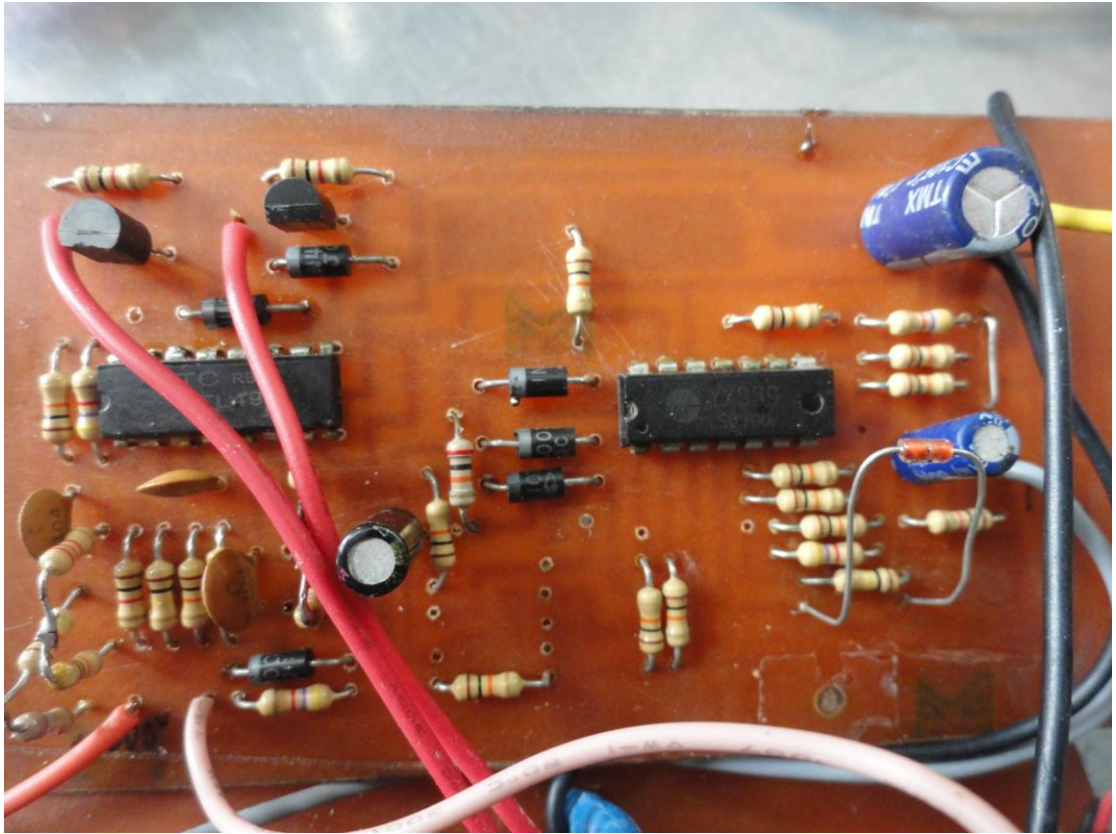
Mạch điều khiển cầu H (Half bridge)
